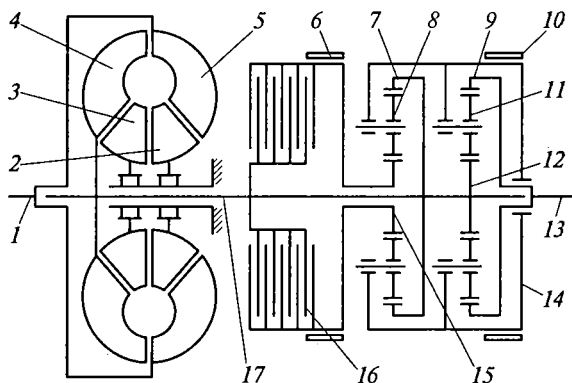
Схема гидромеханической передачи автомобиля ЗИЛ-111:
